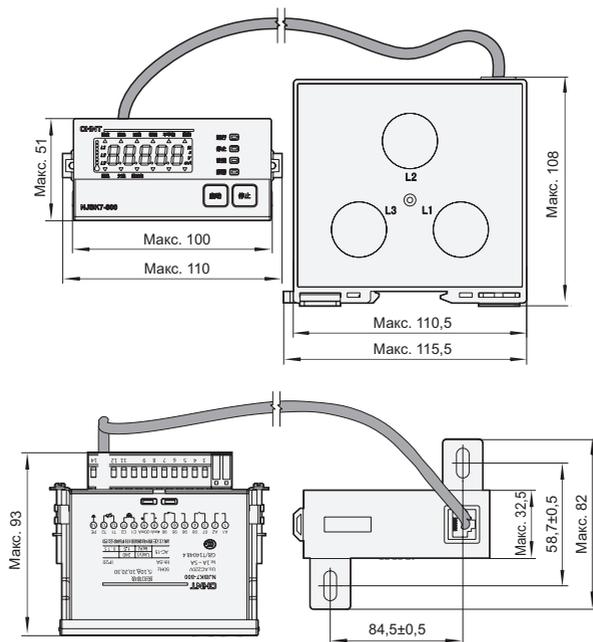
Габаритные и установочные размеры устройства защиты с номинальным током 100 А
